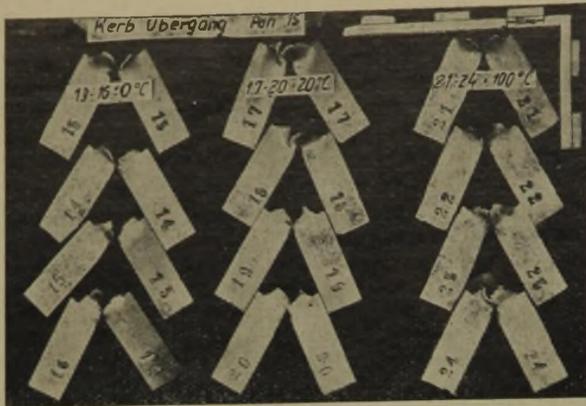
Kerbschlagproben aus dem Schweißgut der „GHH-Pan 15“
